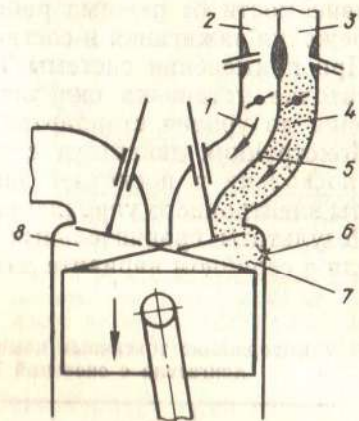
Конструктивная схема двигателя с бесфоркамерным факельным дожигом: 1; 4 — впускные каналы; 2; 3 — камеры карбюратора; 5 — перегородка во впускном канале; 6 — свеча зажигания; 7 — полость богатой смеси; 8 — полость бедной смеси
